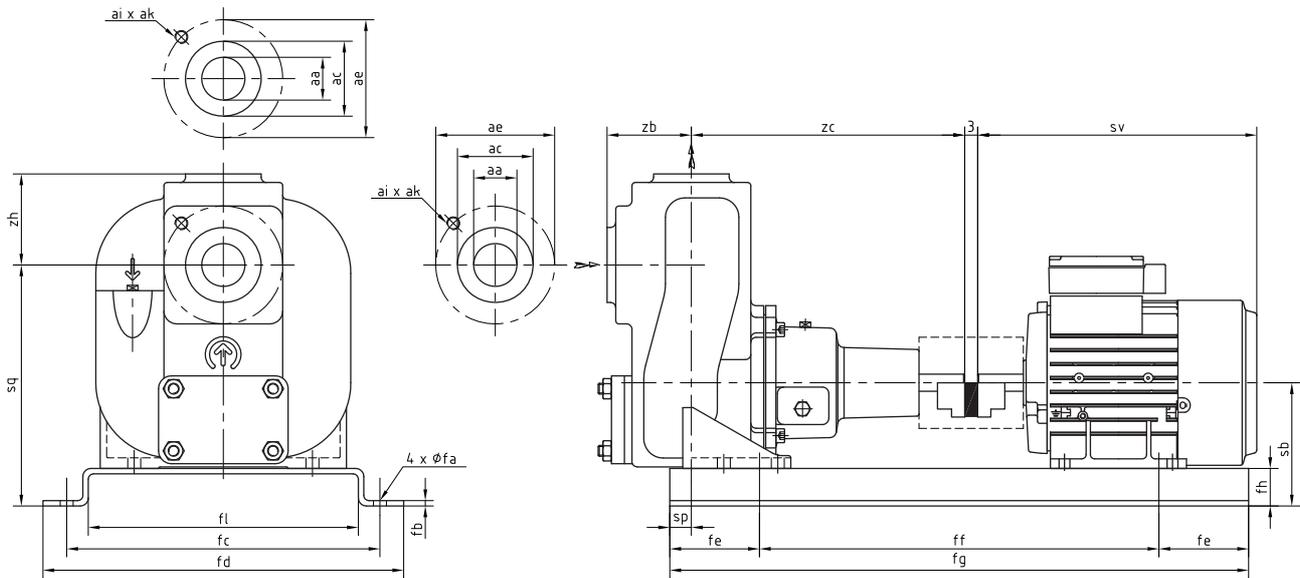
FRE - Pumpenaggregat A6, mit ISO 7005 PN20 Anschlüssen.
